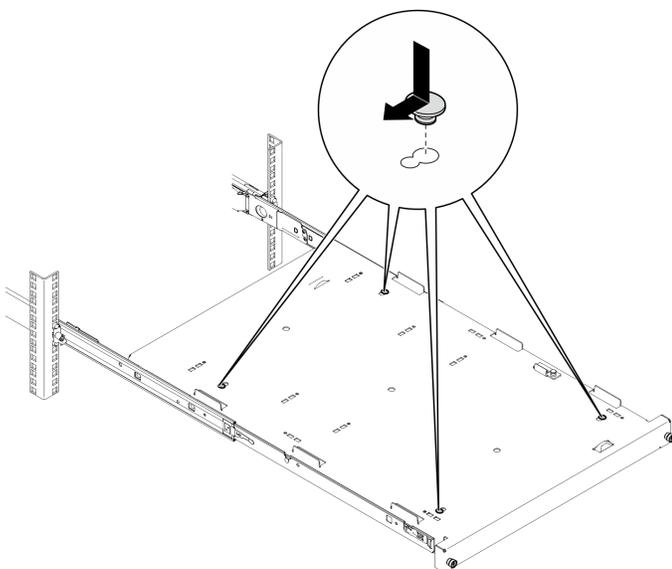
Installation des pieds de sécurité en caoutchouc dans le plateau
